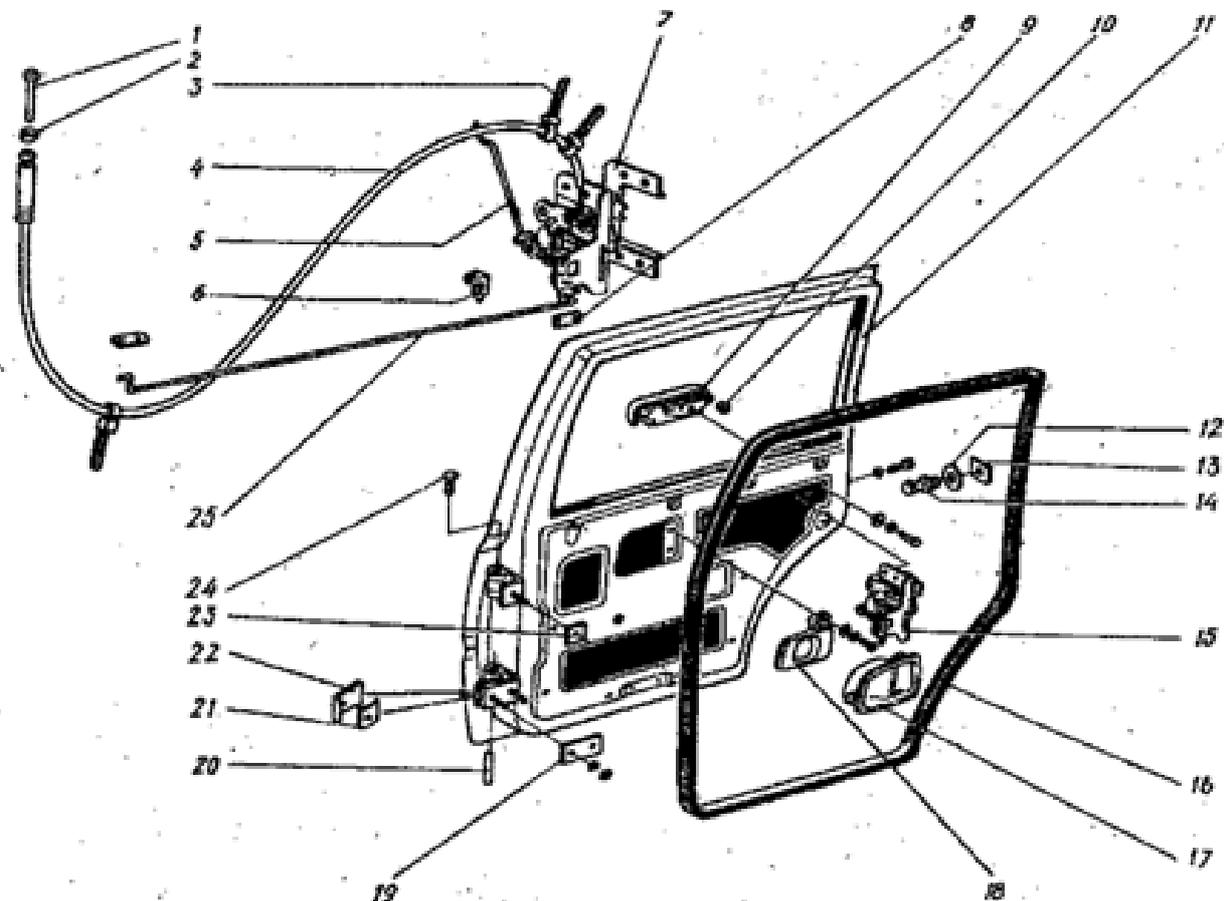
Задняя боковая дверь (без стеклоподъемника) пятидверного автомобиля: 1 - кнопка выключения замка двери; 2 - розетка кнопки; 3 - фиксатор обложки; 4 - обложка тяги кнопки выключения замка двери; 5 - тяга привода наружной ручки; 6 - фиксатор тяги; 7 - усилитель замка двери; 8 - фиксатор тяги внутренней ручки; 9 - ручка двери наружная; 10 - втулка тяги; 11 - дверь с петлями в сборе; 12 - шайба фиксатора замка; 13 - пластина фиксатора замка; 14 - фиксатор замка двери; 15 - замок двери; 16 - уплотнитель двери; 17 - облицовка внутренней ручки; 18 - внутренняя ручка двери; 19 - пластина; 20 - ось петли; 21 - пружина; 22 - фиксатор ограничителя двери; 23 - пластина; 24 - заглушка; 25 - тяга привода внутренней ручки двери.
